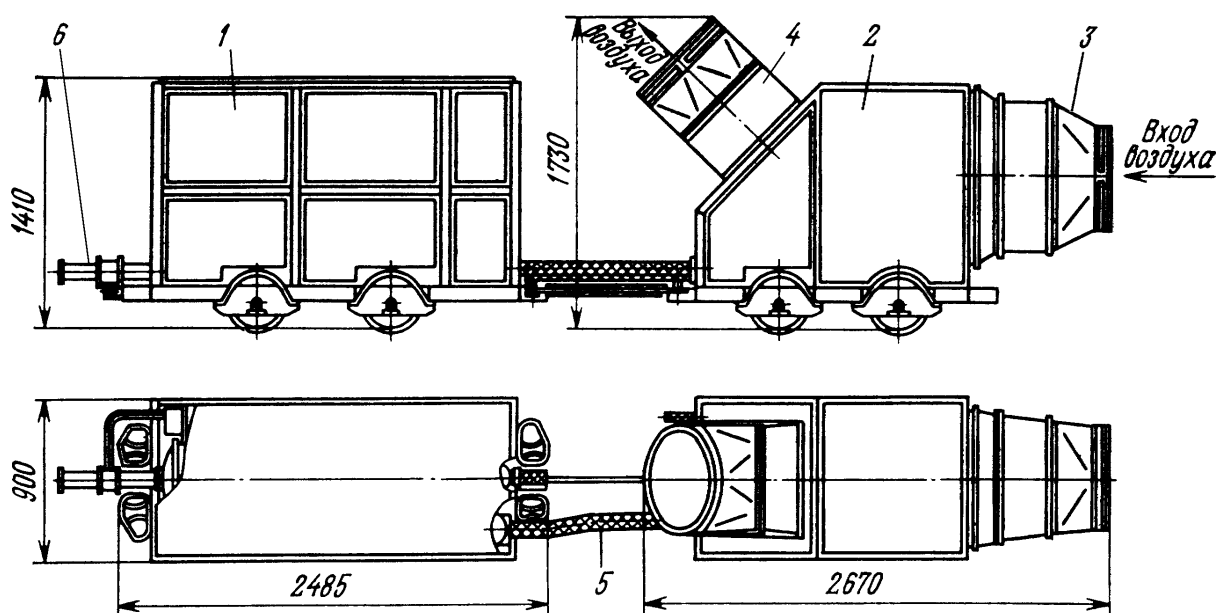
Кондиционер КПШ-90: 1 – компрессорно-конденсаторный агрегат; 2 – воздухообрабатывающий агрегат; 3 – патрубок входа охлаждаемого воздуха; 4 – патрубок выхода охлажденного воздуха; 5 – гибкие рукава для жидкого и газообразного хладагента; 6 – патрубки подвода воды
